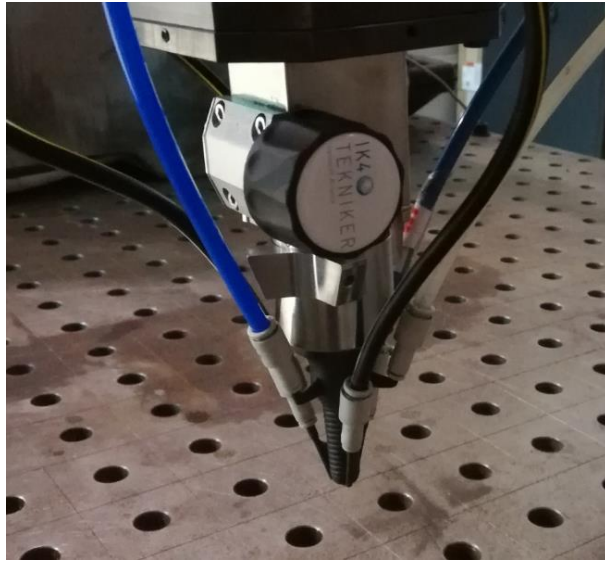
Boquilla de aporte desarrollada en TEKNIKER.
